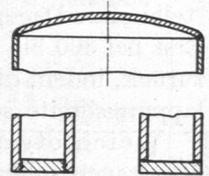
bis 609. Unrichtige Lage der Schweißnähte, die starken Nebenbeanspruchungen auf Zug und Biegung ausgesetzt sind.
